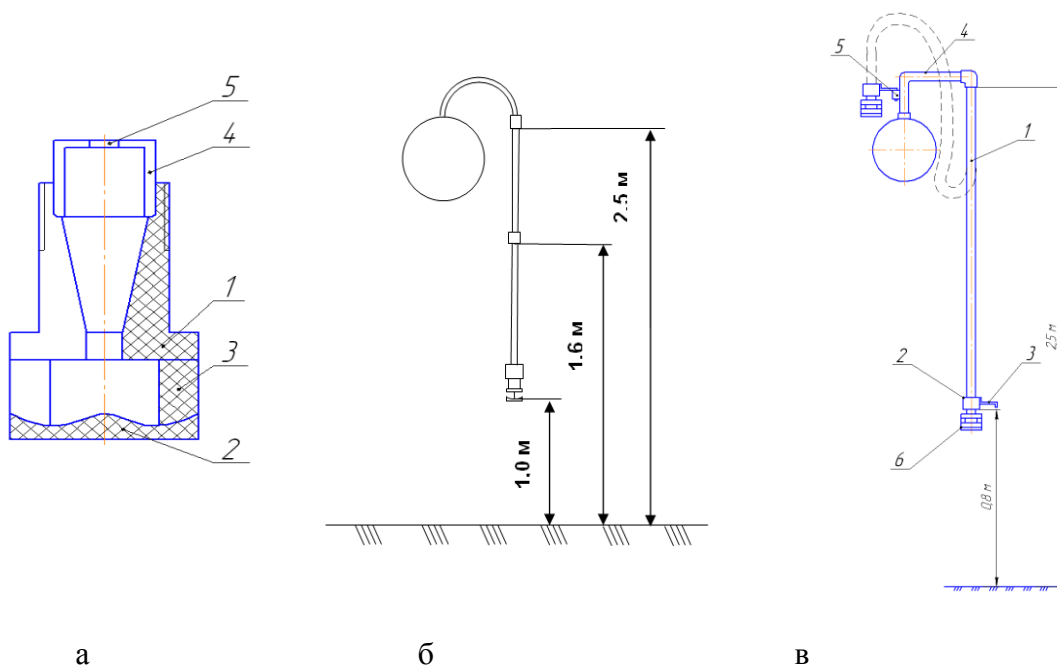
Дождевальная насадка с дефлектором «обратный конус» (а) и устройства приповерхностного полива типа «сборная штанга» (б) и «сборный рукав» (в)
